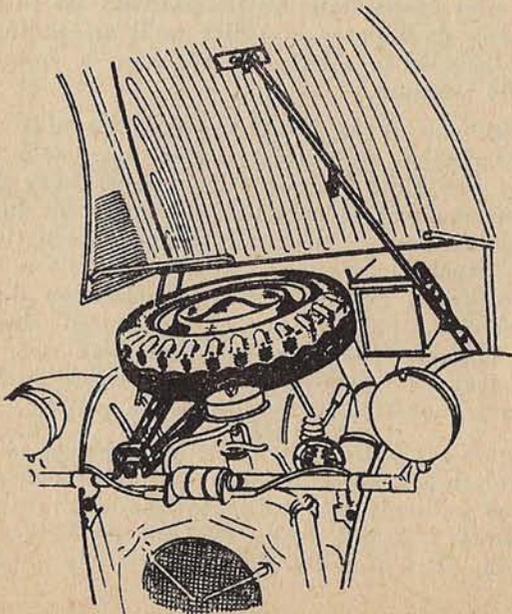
Support de roue de secours pour installation sous capot, accroissant le volume du coffre arrière (VW)
